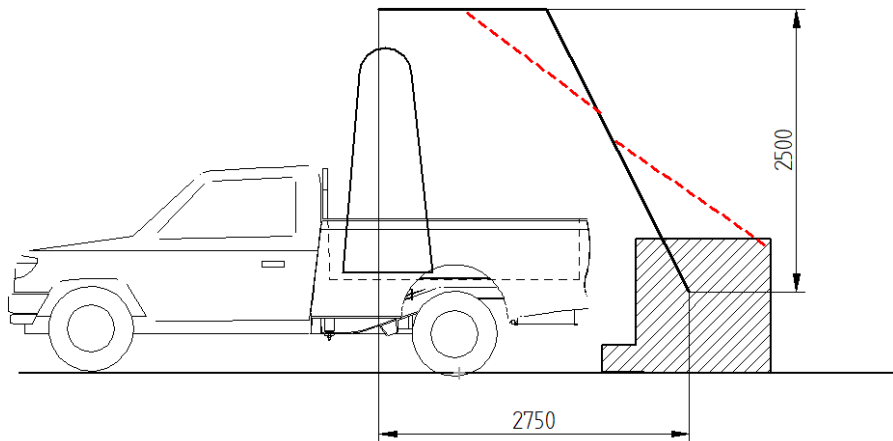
Esboço com dimensões alvo. O equipamento deveria ser capaz de içar a carga de um pedestal de altura de 800mm e posicioná-la na caçamba de uma caminhonete o mais próximo possível da cabine (Elaboração própria)
